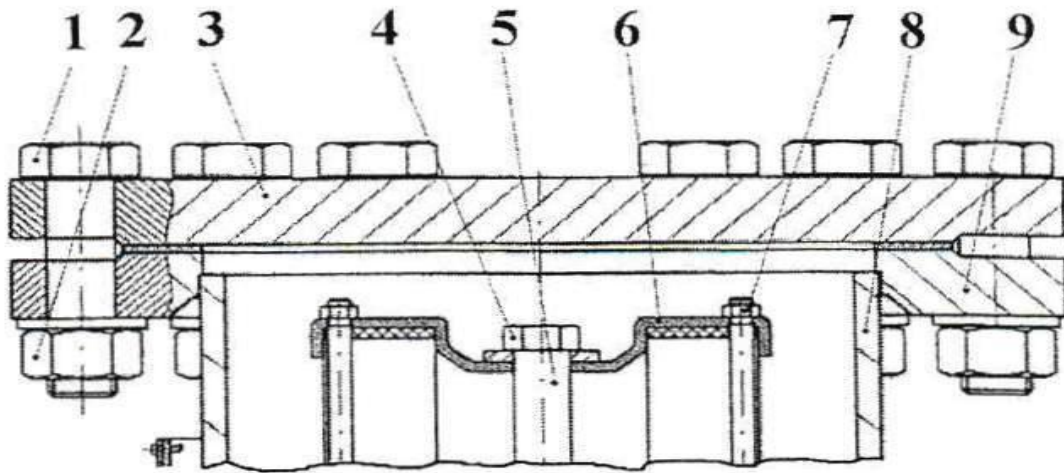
Detaliu închidere filtru cu flanșe oarbe
